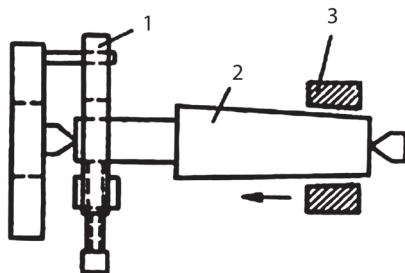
Притирка кольца к конусу на токарном станке:
